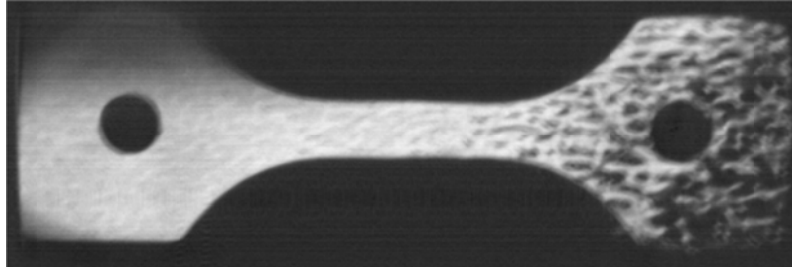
Vista en planta de la reconstrucción digital de la muestra 48_12.
